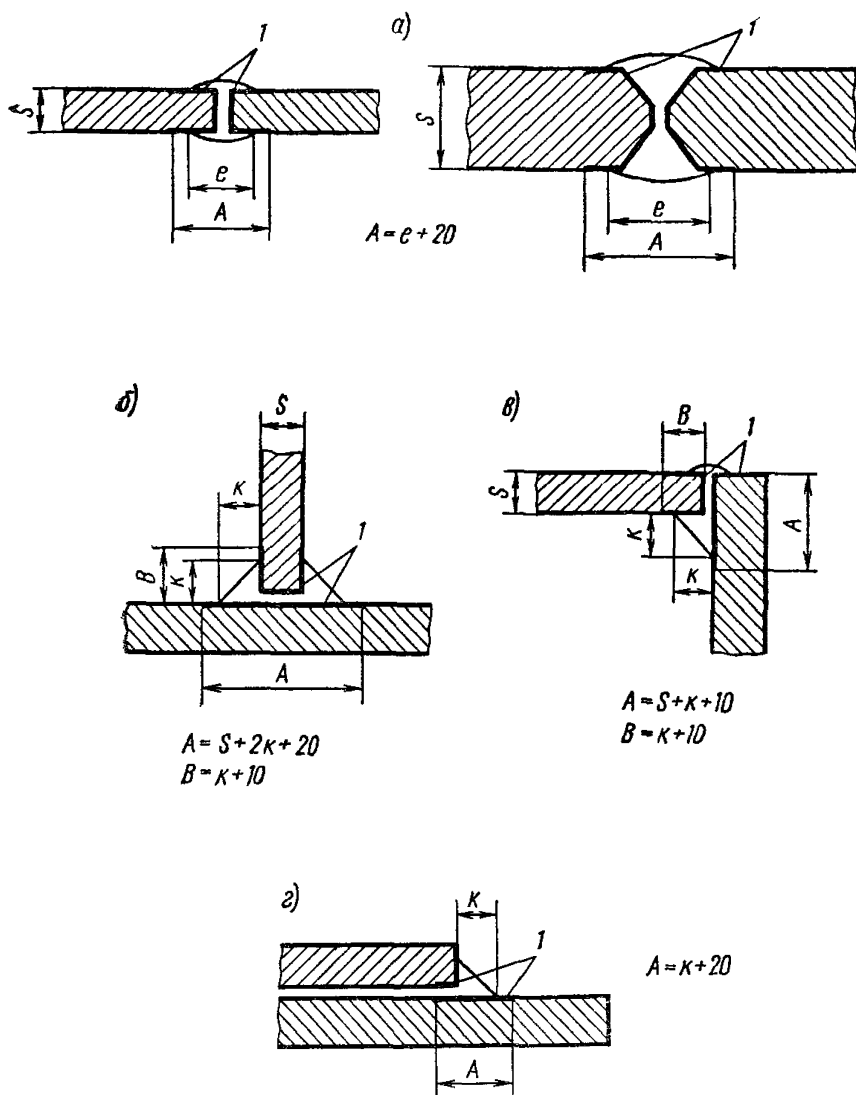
Схема зачистки кромок и поверхности металла сварных соединений:
